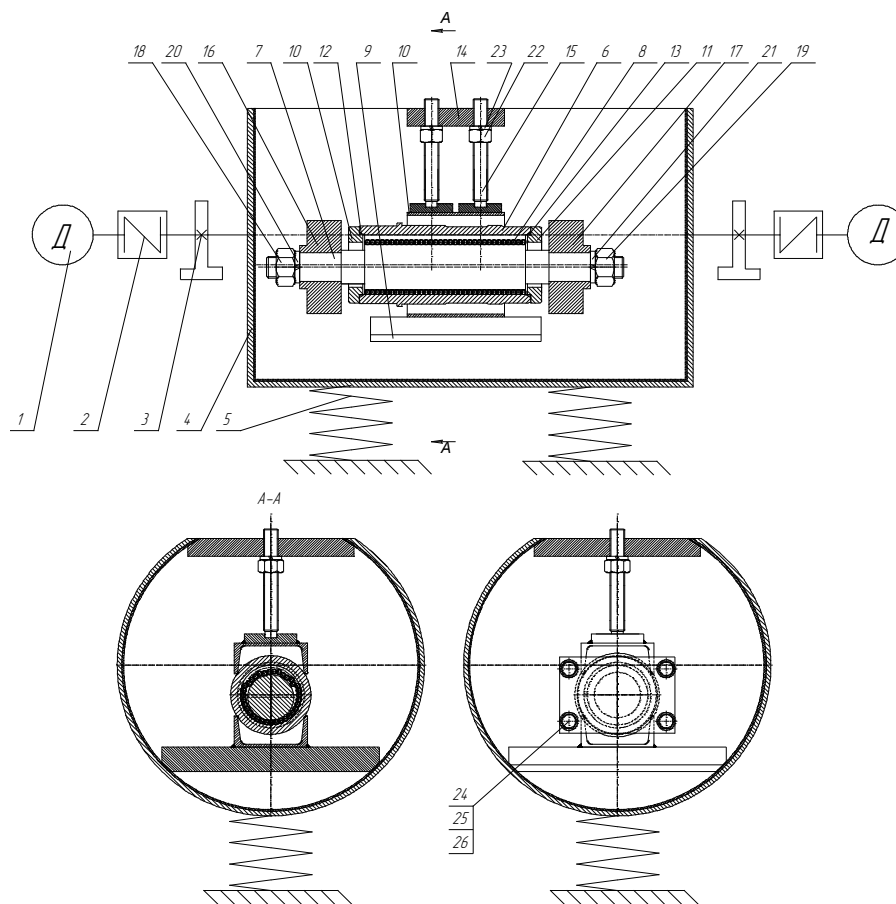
Принципова схема технологічного обладнання для вібраційного оброблення
